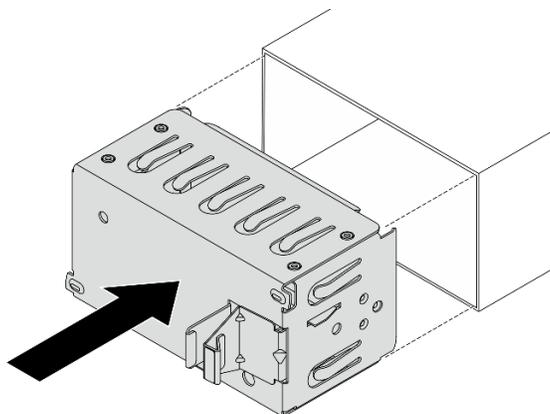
Installazione dell'elemento di riempimento dell'unità di alimentazione
